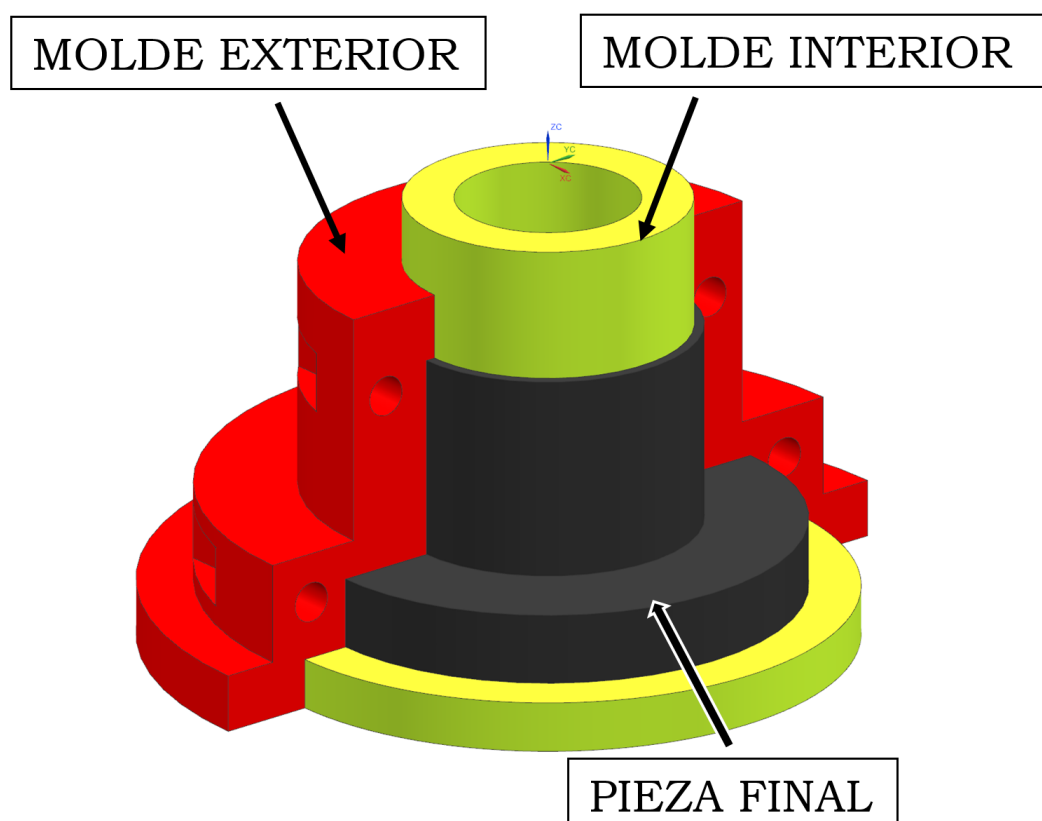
Diseño del Molde. Piezas que componen el molde. (Fuente: Propia)
